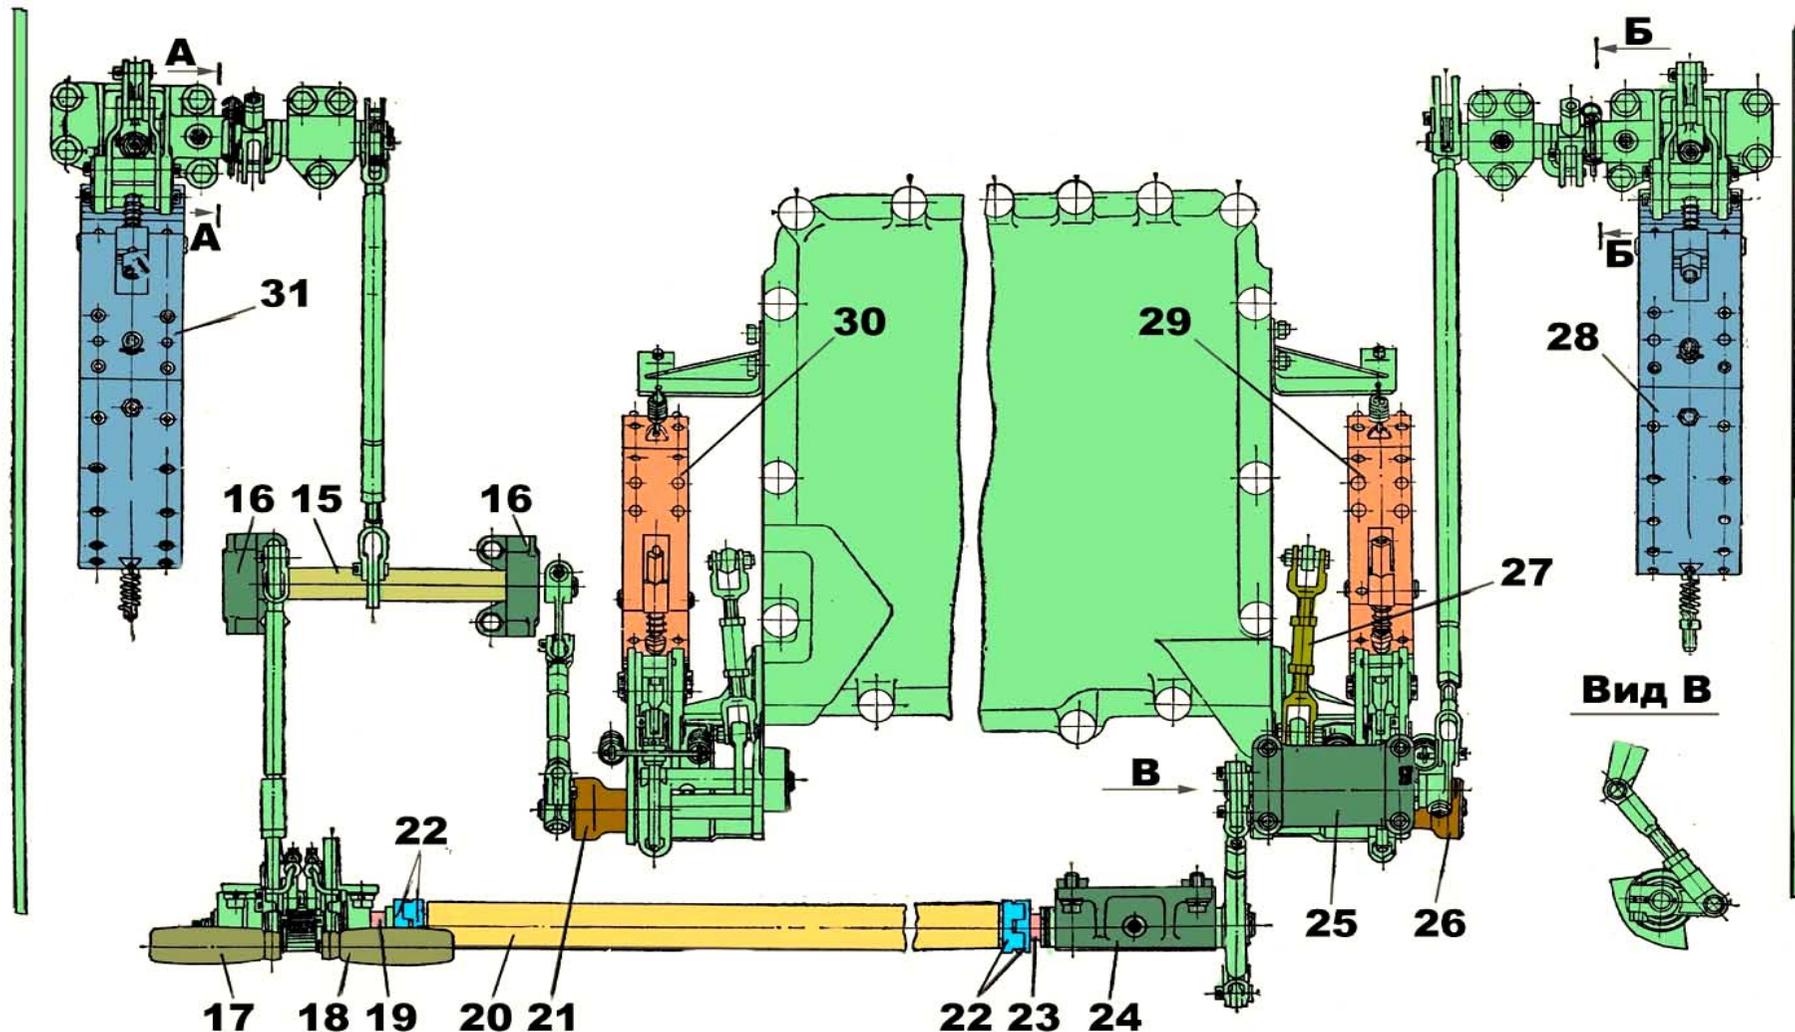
Привод управления остановочными тормозами и планетарно-фрикционными механизмами поворота:
